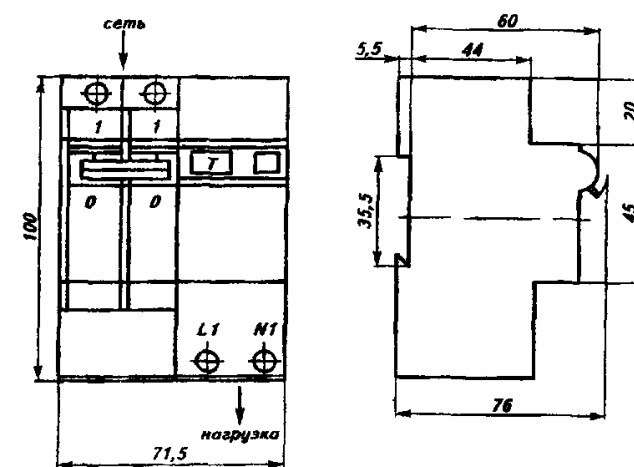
Общий вид, габаритные и установочные размеры устройства защитного отключения УЗО20-ВАД2
